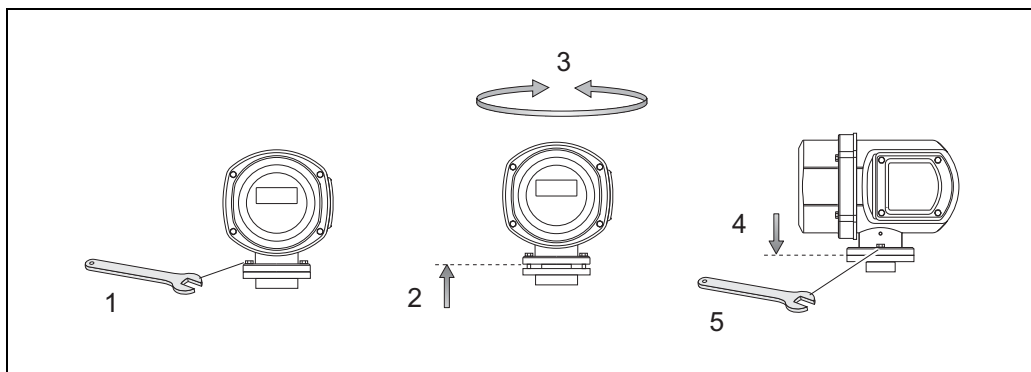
Поворот корпуса преобразователя из нержавеющей стали, погружаемого в среду
